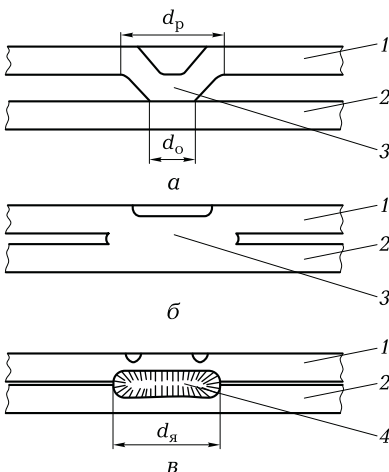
Стадии (а–в) формирования рельефно-сварного соединения:
